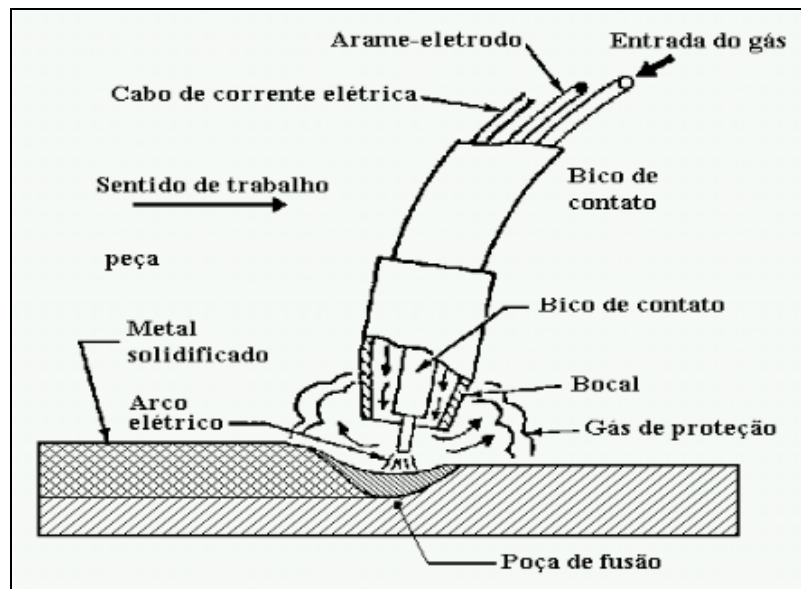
Esquema do processo de soldagem MIG/MAG.
